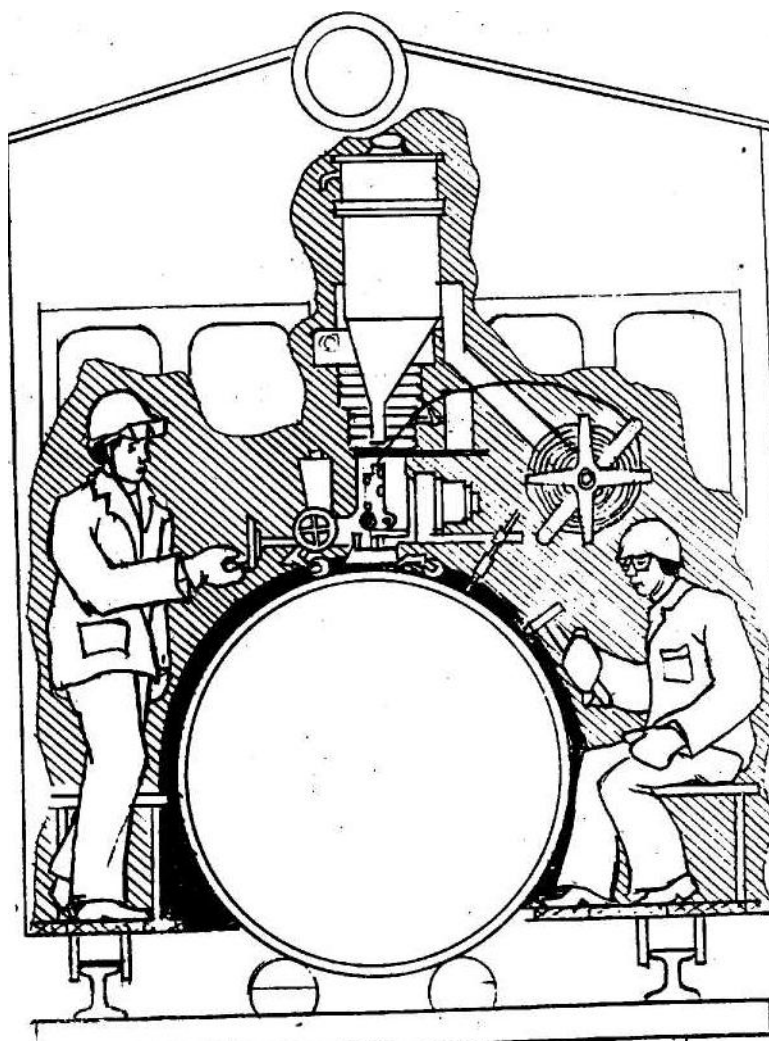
Сварка заполняющего слоя
